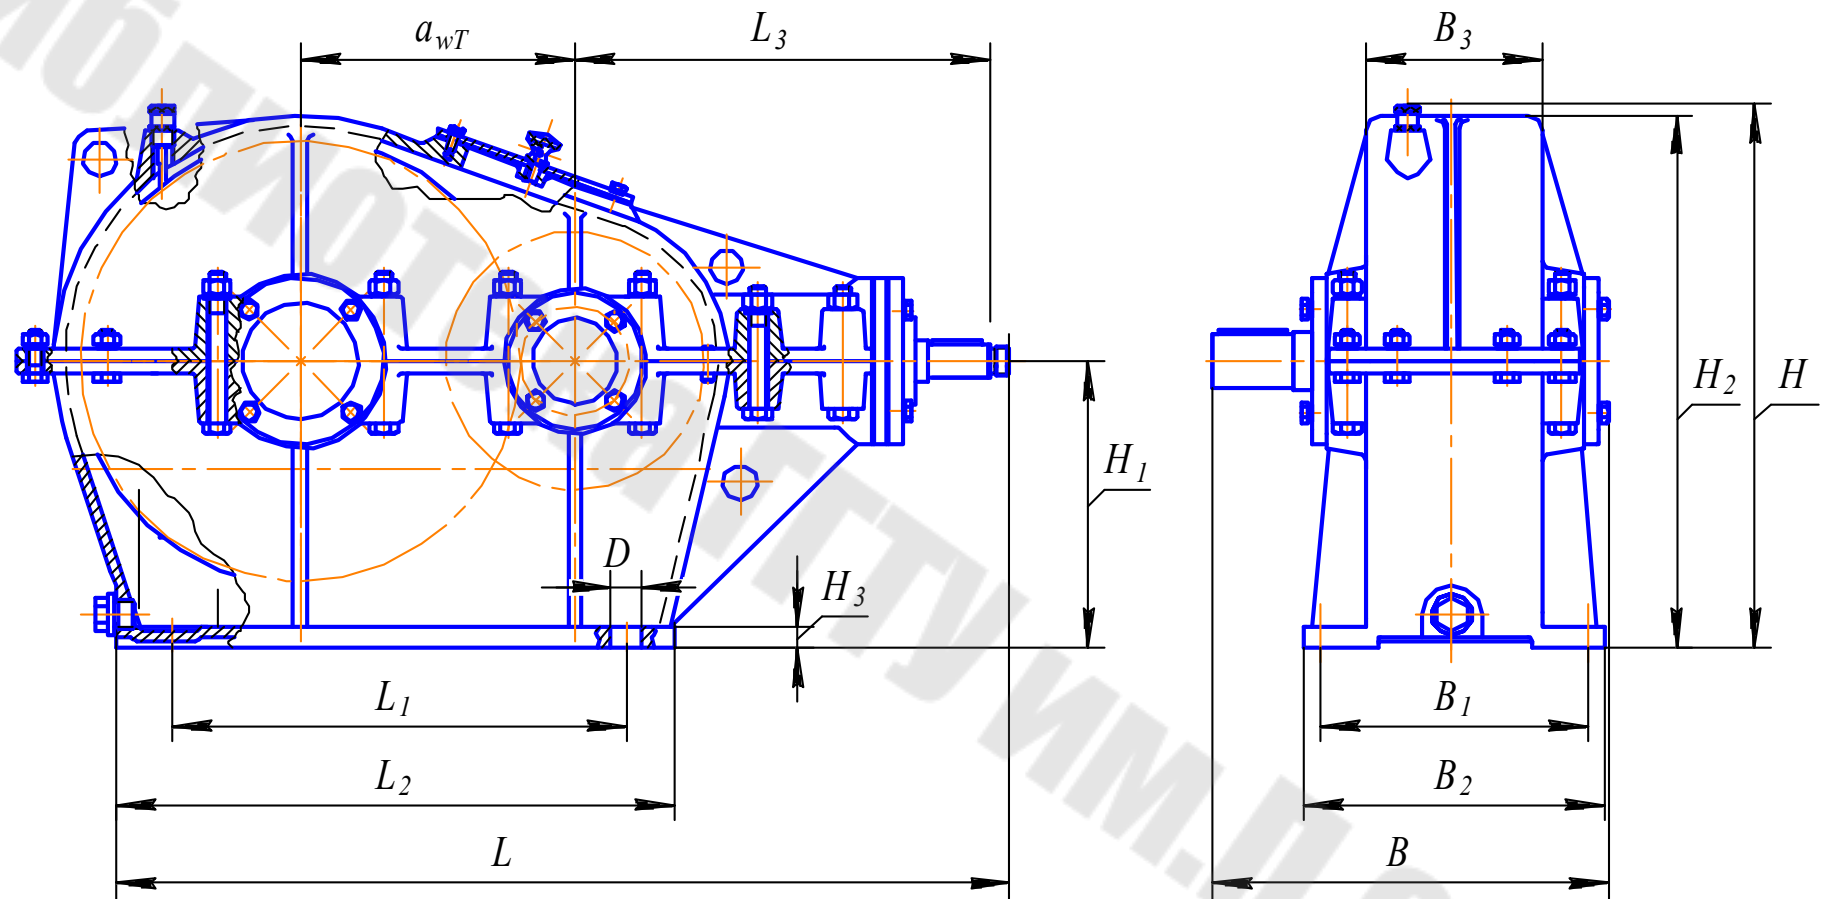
Габаритные и присоединительные размеры коническо-цилиндрического редуктора
